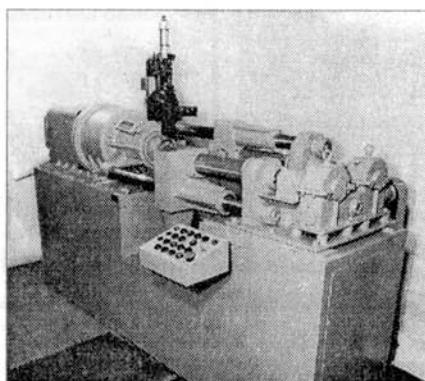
Машина СТ-109А для инерционной сварки трением
